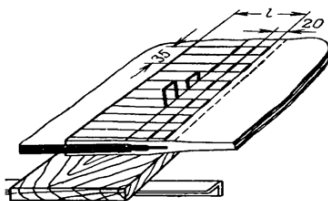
Скрепление концов ленты П-образными скобами [2]
